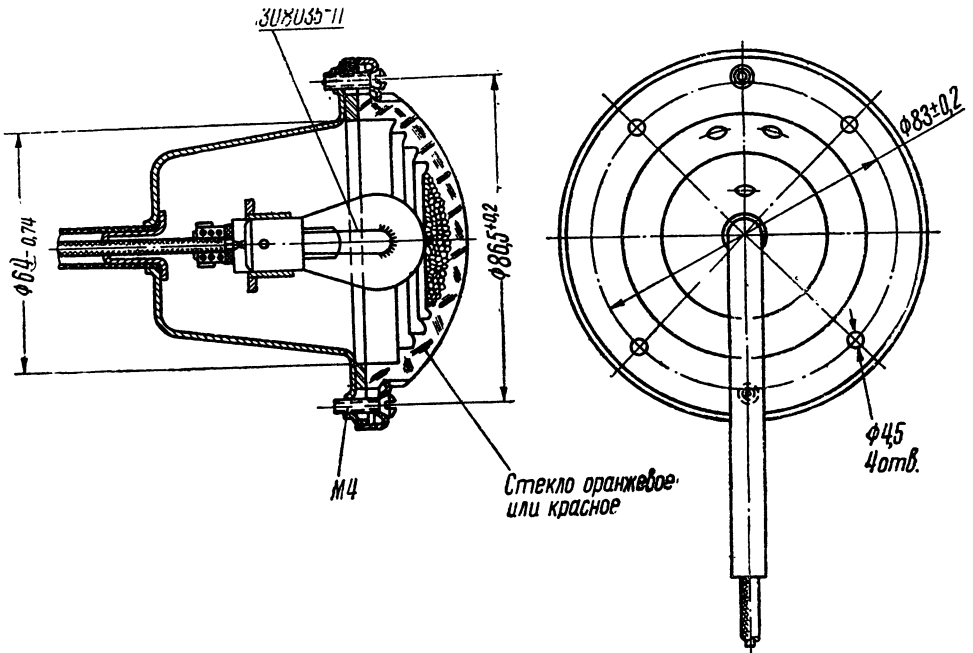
Задний указатель поворота автобуса ЗИЛ-158
